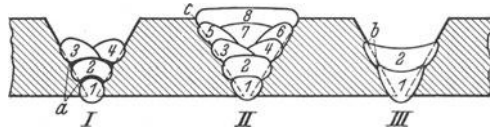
Aufbau der V-Schweißnaht.
